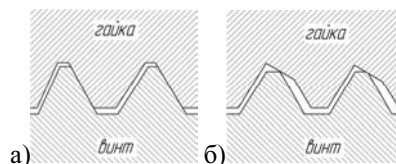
Профили а – стандартной и б – “EMUGE-SPIRALOCK” резьбы
